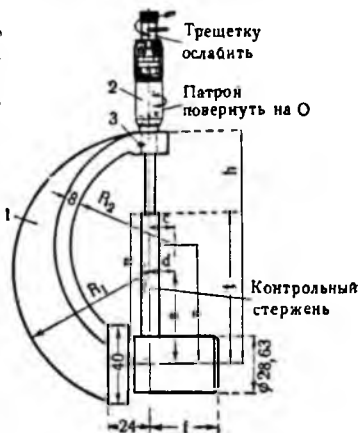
Специальный микрометр для установки резцов в резцовых головках станков для расточки цилиндров:
